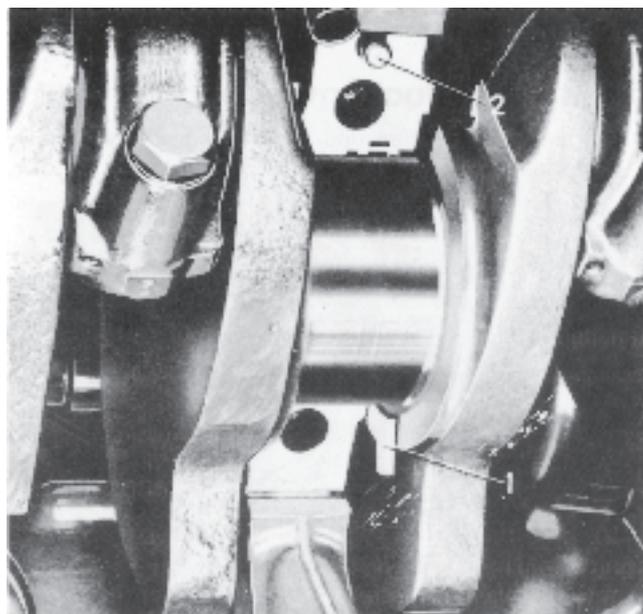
Languette (1) de fixation et goupille (2) de positionnement pour chapeau de palier
